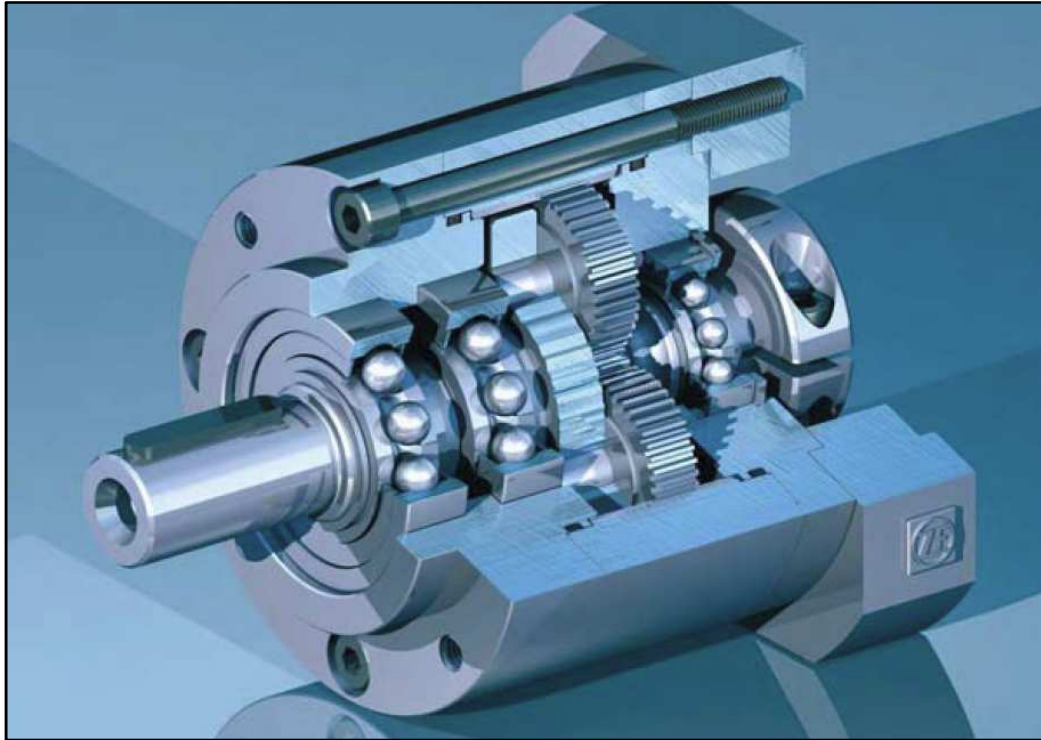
Reductor *ZF Maschinenantriebe GmbH PGE25/1 i=10*.
